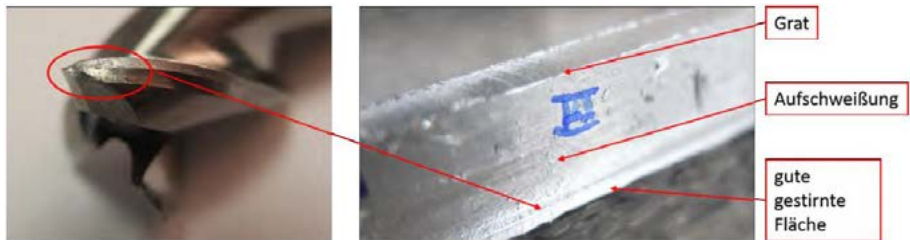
Materialaufschweißungen am Fräser und auf dem Steg, Höhe 60mm
